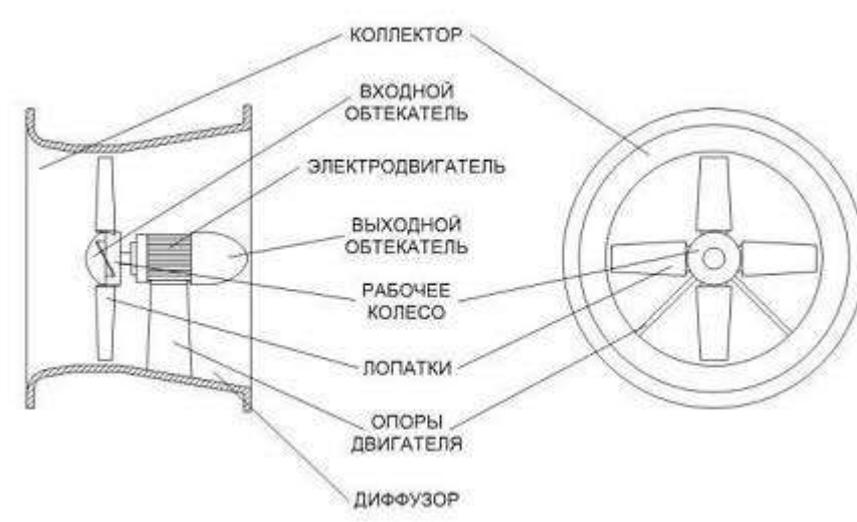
Конструктивный вид осевого вентилятора.
